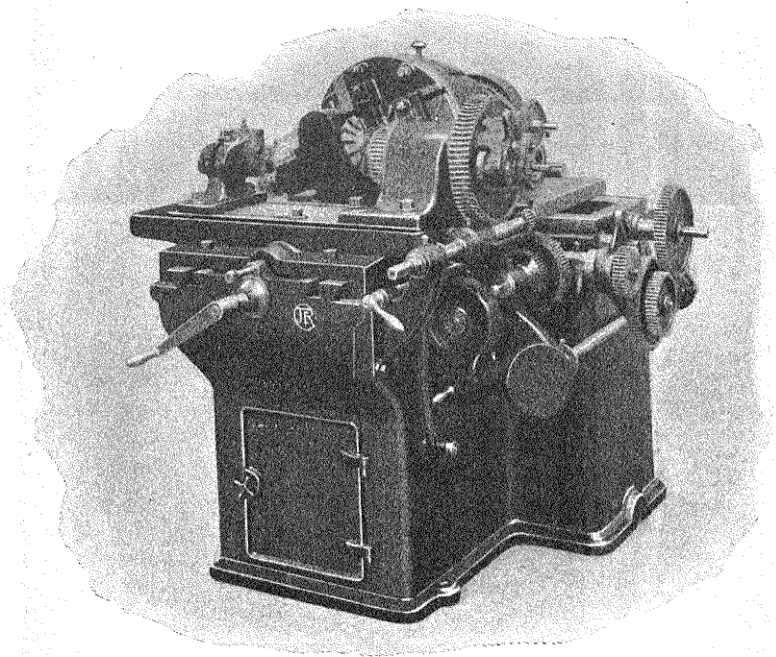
Machine à fraiser les vis sans fin Reinecker.
